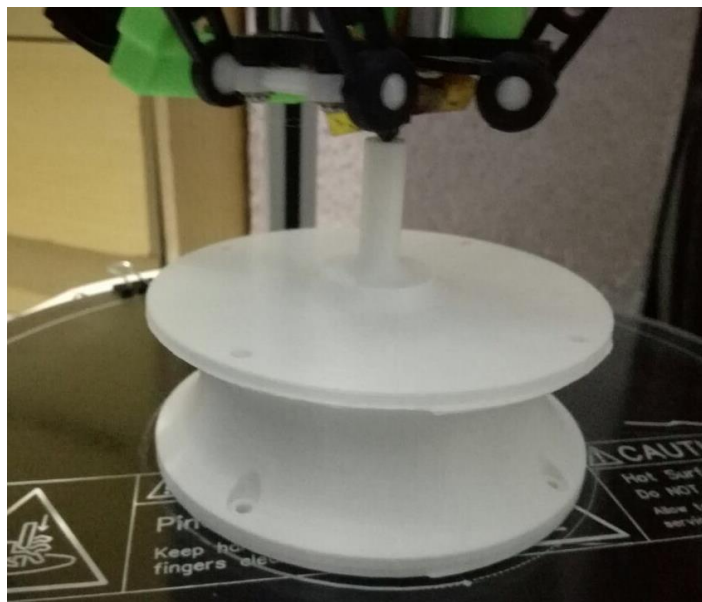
Impresión del difusor de aire. Final de la impresión por la parte inferior del difusor.
